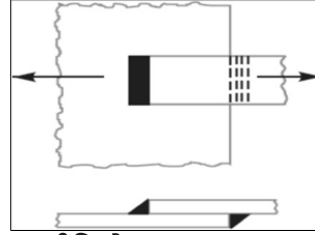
डबल ट्रान्सव्हर्स फिलेट (Double Transverse Fillet Weld)
